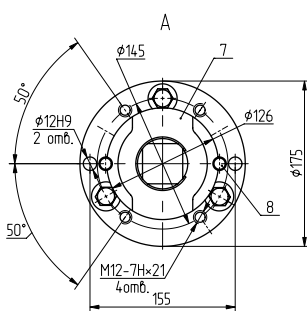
Габаритные и присоединительные размеры М30Ф-2500
